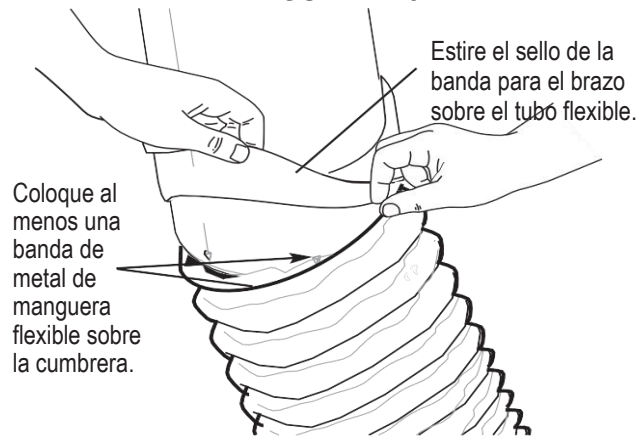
COLOCACIÓN DE LA MANGUERA AL CONJUNTO DE MONTAJE: K1655-14
